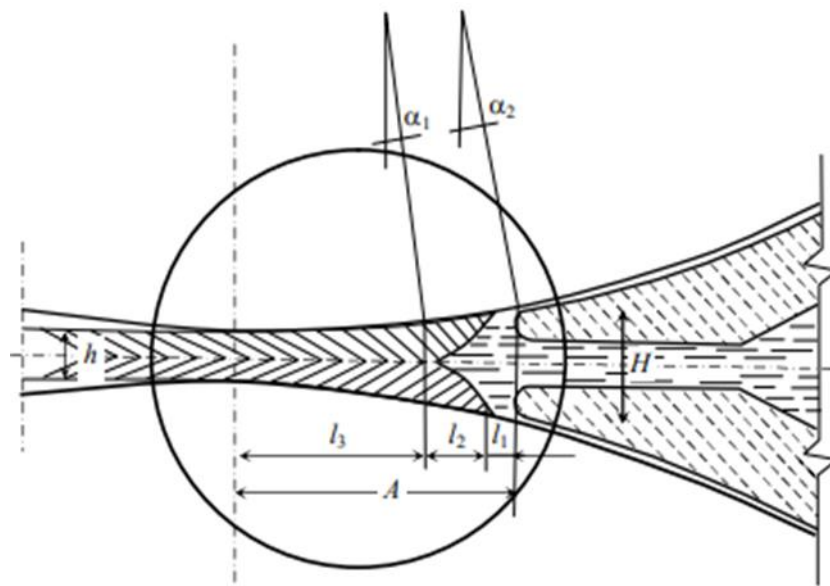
Схема зони лиття та прокатки при двовалковій розливці металів
